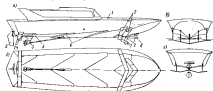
Схема крыльцового устройства и выступающих частей катера «Чайка»: а — вид сбоку; б — вид на деке; в — ХХХ по нос; с — вид на корпус; 1 — корпус; 2 — стойка штурвала в кормовом крыле; 3 — палец; 4 — кормовый киль; 5 — кормовый транец; 6 — редан; 7 — носовое крыло; 8 — длинноствольное штуртросовое устройство.
